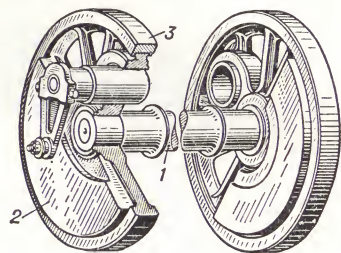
Колёсная пара: 1 — ось; 2 — колёсный центр; 3 — бандаж.
